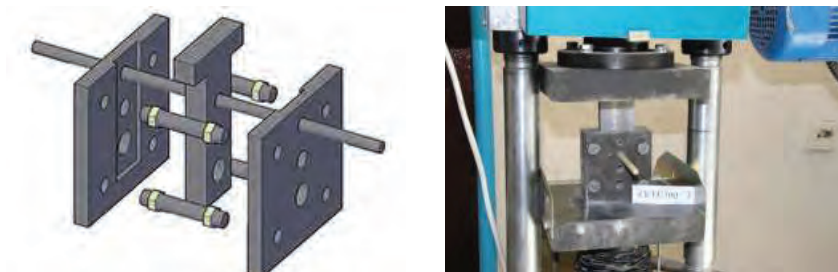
Оснастка для испытаний гибких связей на поперечный срез и общий вид испытаний
